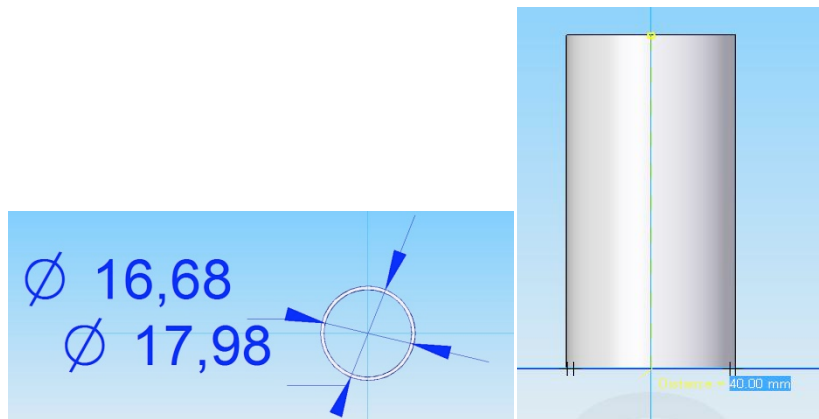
Dimensiones del molde utilizando tubo de acero
